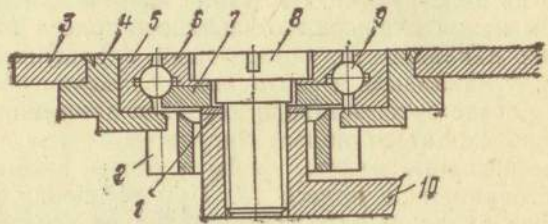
Схема шарикоподшипника в часах с автоподзаводом пружины:
